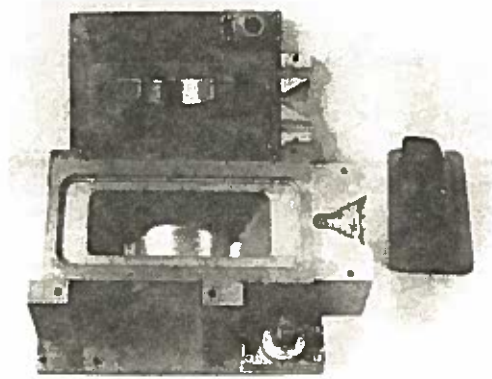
Spritzpreßform für 300 mm langes Sichtfenster
